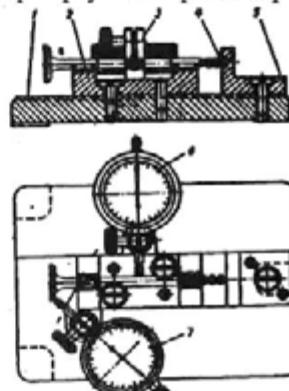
Приспособление для проверки биения рабочей фаски и стержня клапана:
